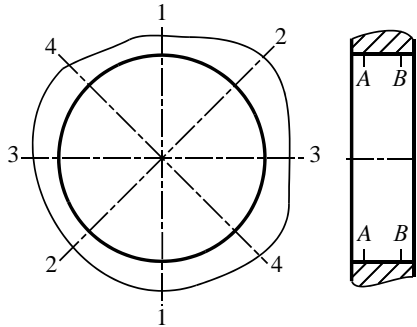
Схема вимірювання отворів корпусних деталей:
